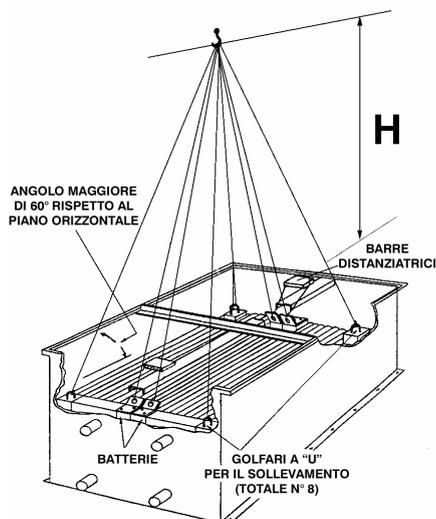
Sezione scambio più larga (n° 2 batterie)
